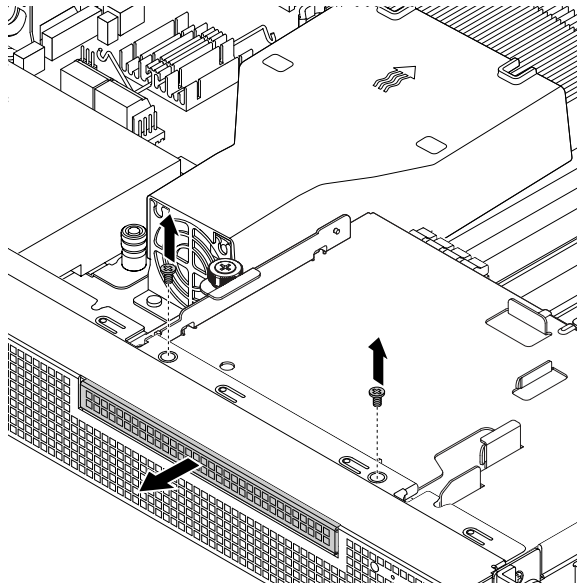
Metallblende der Position für das optische Laufwerk entfernen
